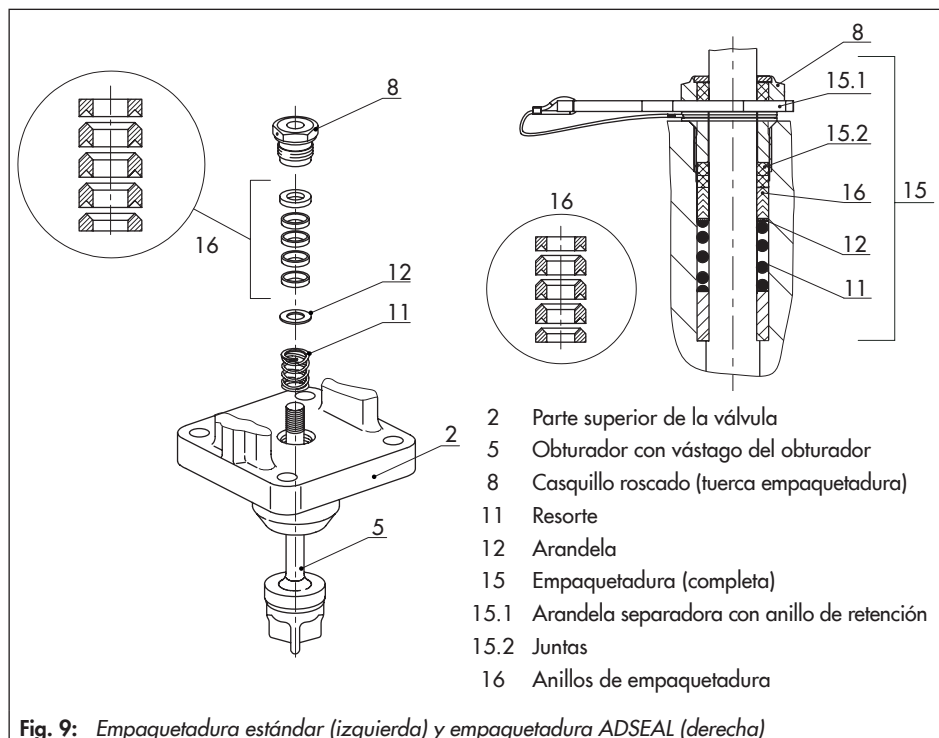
Empaquetadura estándar (izquierda) y empaquetadura ADSEAL (derecha)
